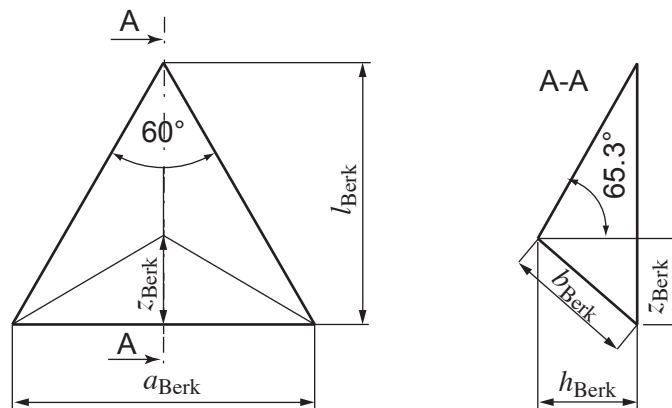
Geometrie des Berkovich-Indenter: Draufsicht (links) und Mittenschnitt (rechts) [8]
